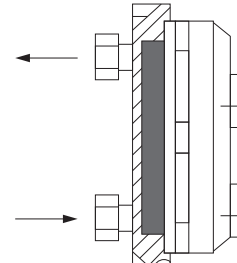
Охладитель с установленным силовым IGBT-модулем, с размерами корпуса 140×130 мм, вид сбоку
